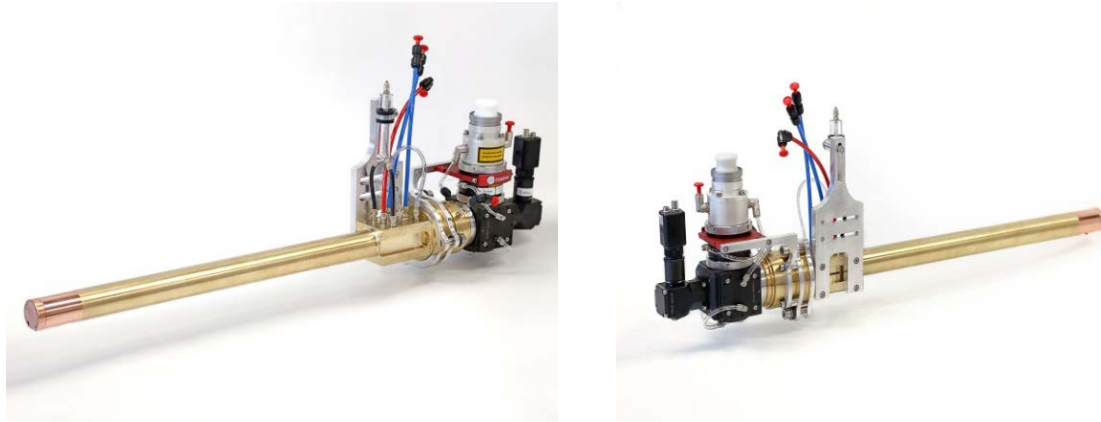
+2: Härten, Beschichten, Legieren – die iClad®-Innenbearbeitungsoptik ermöglicht ab 30 Millimetern Innendurchmesser das gesamte Spektrum der Innenkonturbearbeitungen.
